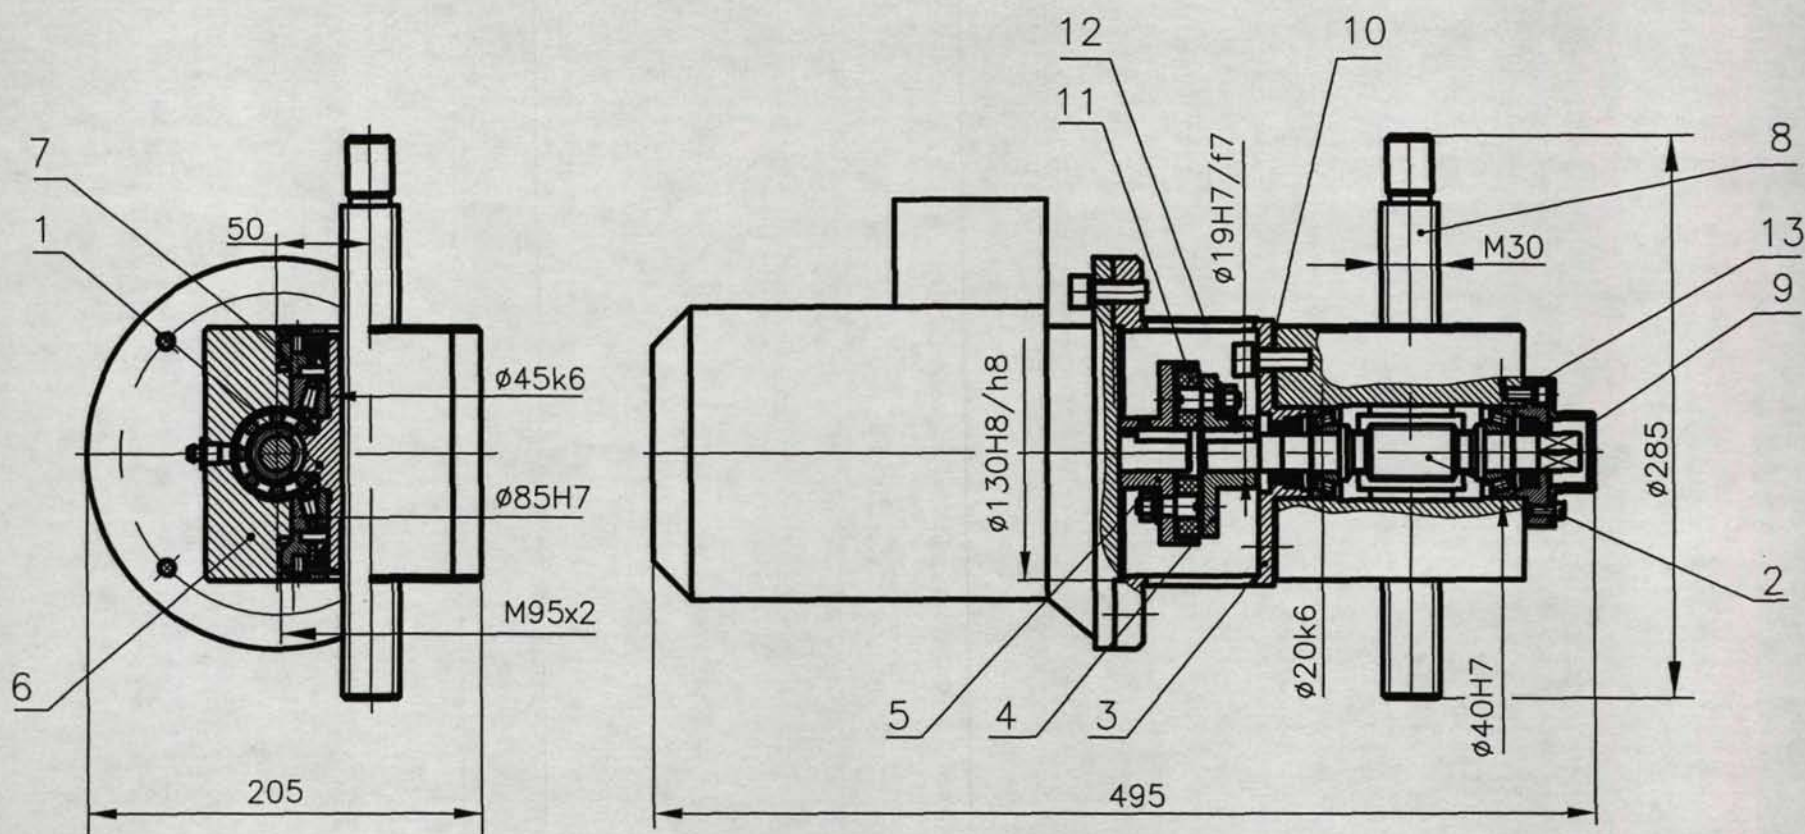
Эскиз сборочной единицы "червячный мотор-редуктор":
